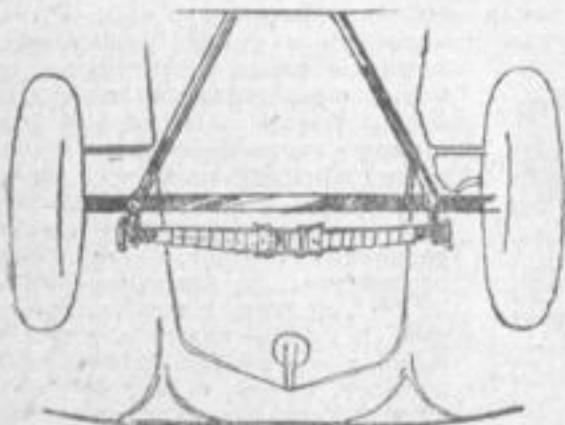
Новая конструкция передней рессоры Форда, установленной на легковых и грузовых машинах. (Рессора грузовика—вид сверху)
